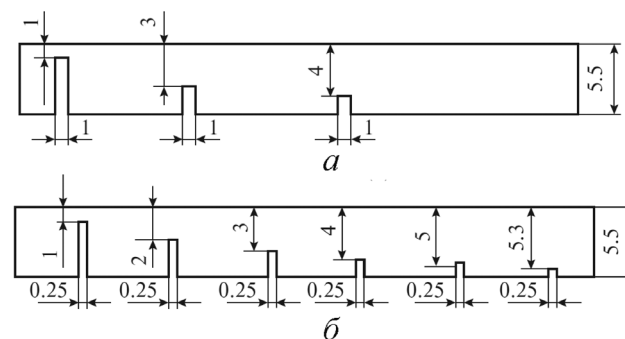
Пластины № 1 и № 2 (вид сбоку)
